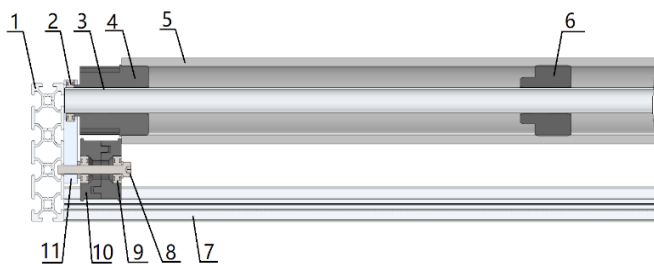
Конструктивно-технологическая схема роликов и их установка на опоры (в разрезе):
